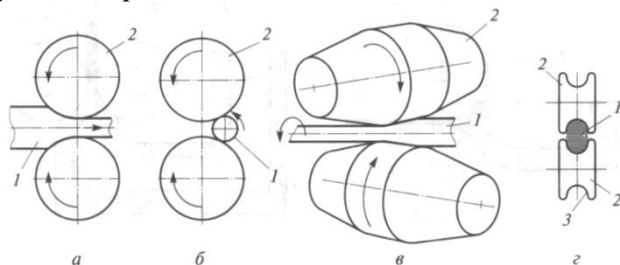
Схемы продольной (а), поперечной (б), винтовой (в) и профильной (г) прокатки: 1 — заготовка; 2 — валки; 3 — профиль валка
